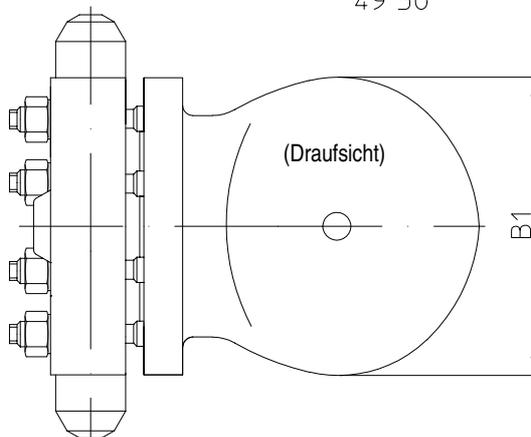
4 mit Schweißenden - horizontale Einbaulage
